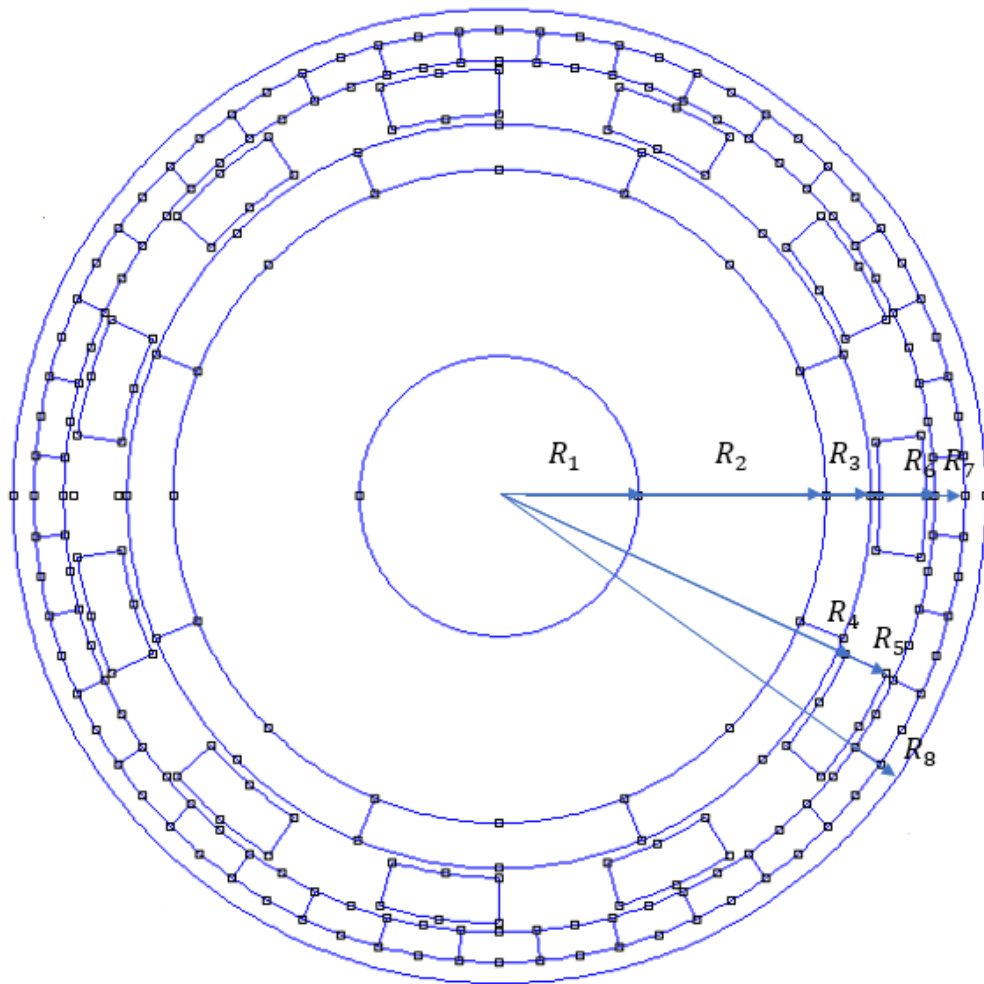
Diseño preliminar del engranaje magnético coaxial
